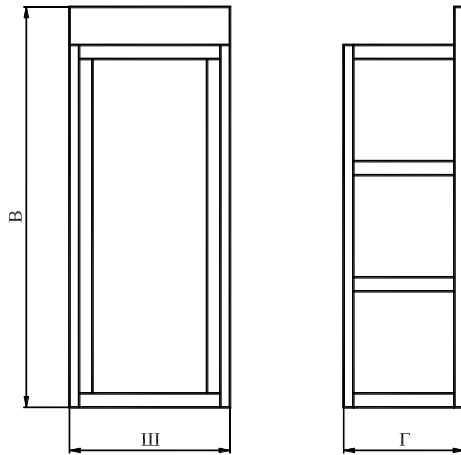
Габаритные размеры корпусов металлических ЩО-70
